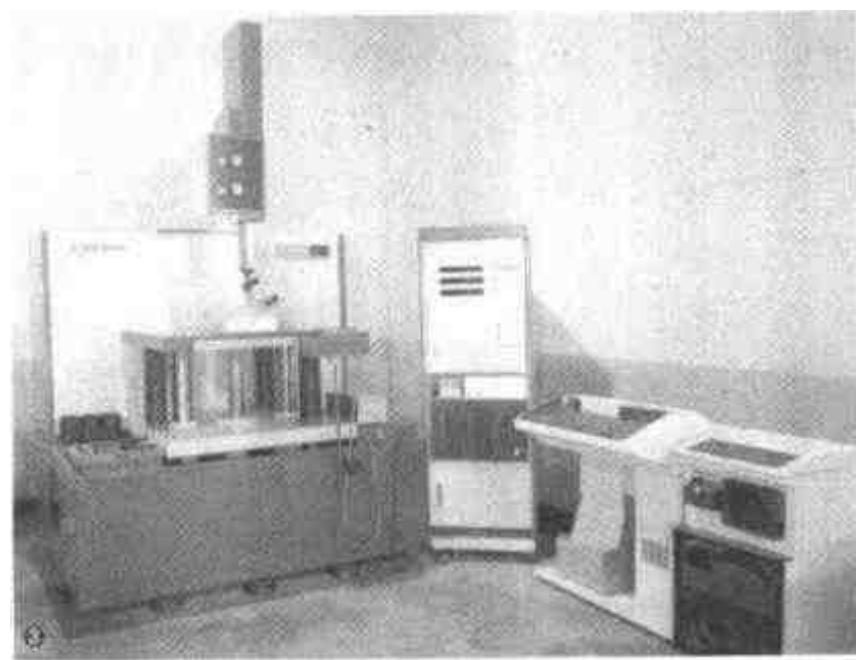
三坐标仪——从模型或实物获得数控加工程序，再通过数控程序的几何数据生成零件图纸
